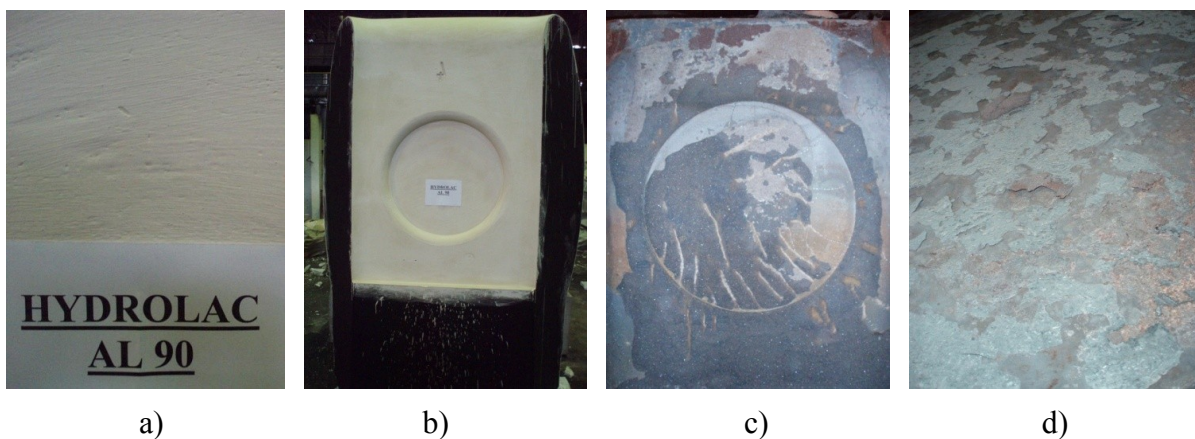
Jádru číslo 2 – a) detail naneseného nátěru, b) detail jádra, c) plocha náboje po odlití, d) detail povrchu odlitku před tryskáním
